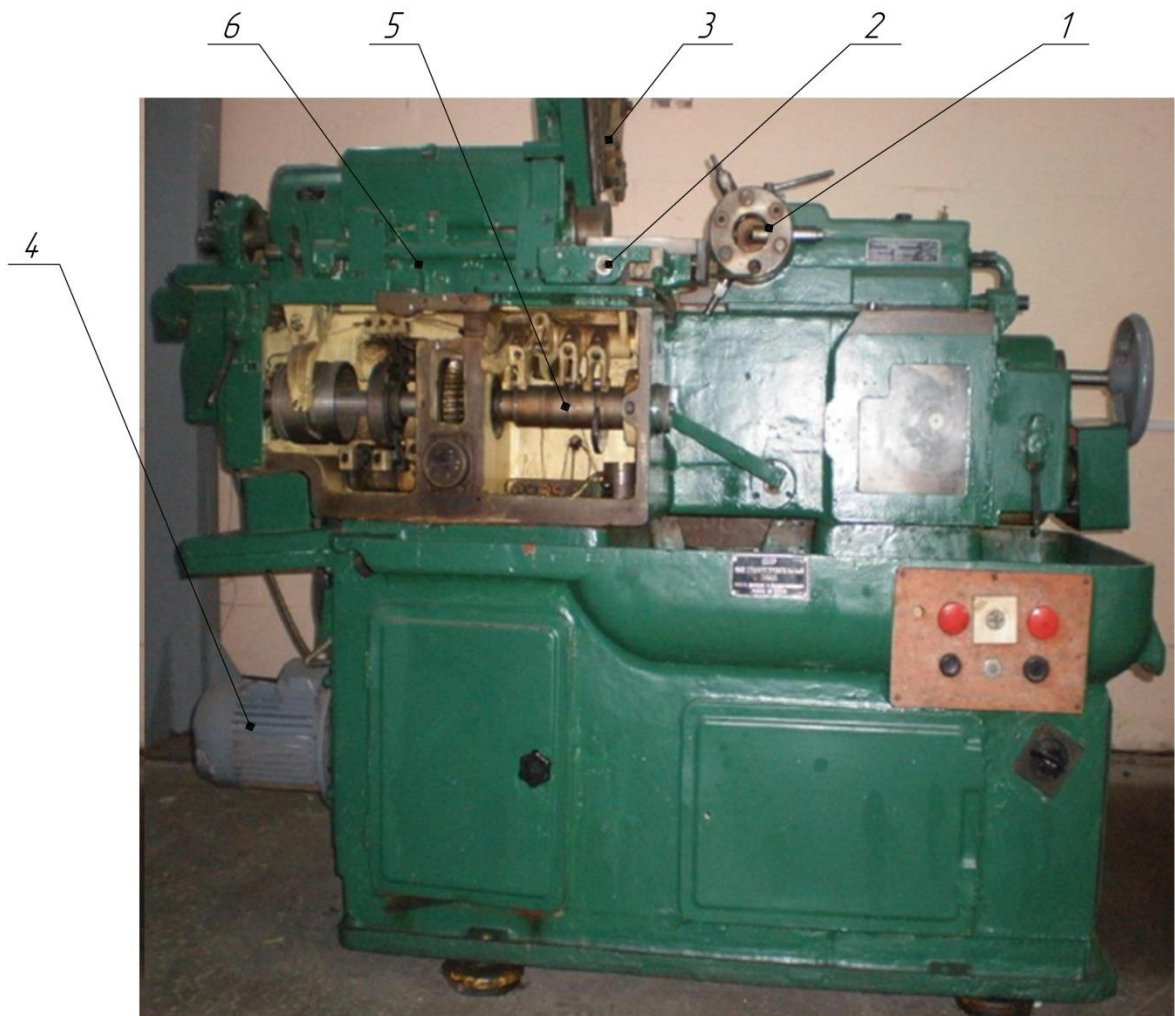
Загальний вигляд токарно–револьверного верстата автомата 1Б140:
